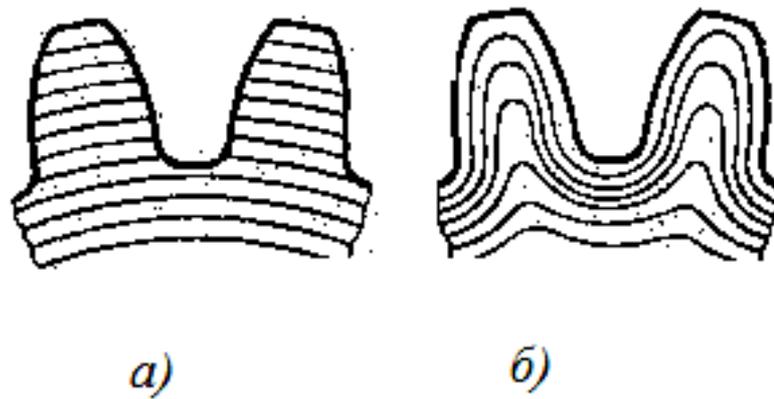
Расположение волокон в зубьях шестерни, полученных механической обработкой (а) и горячей накаткой (б)
